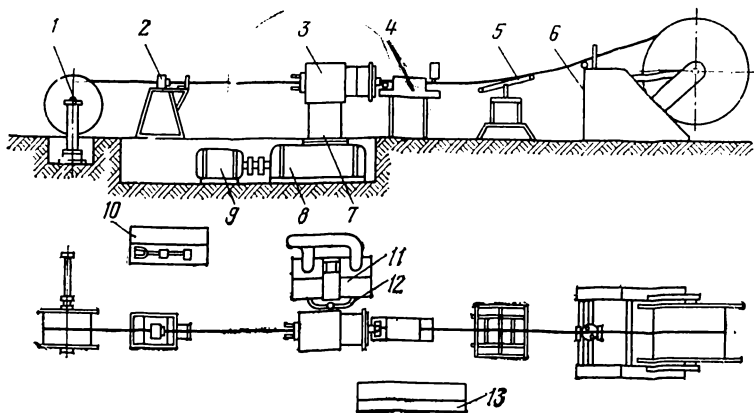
Схема агрегата наложения свинцовой оболочки на червячном прессе.
